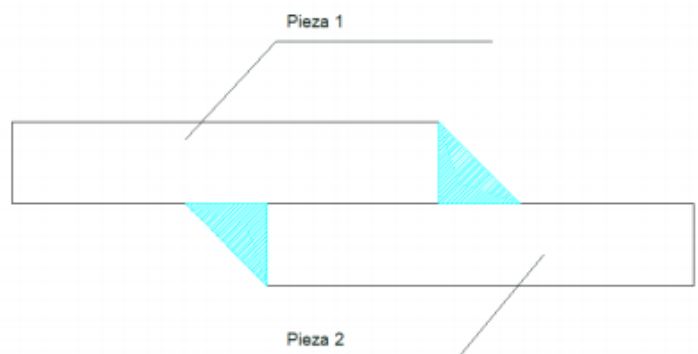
Soldadura Traslapada doblemente soldada.
